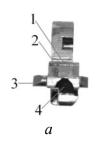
Шептало: 1 – зуб шептала; 2 – носик шептала; 3 – стойка; 4 – пружина шептала; 5 – цапфа
